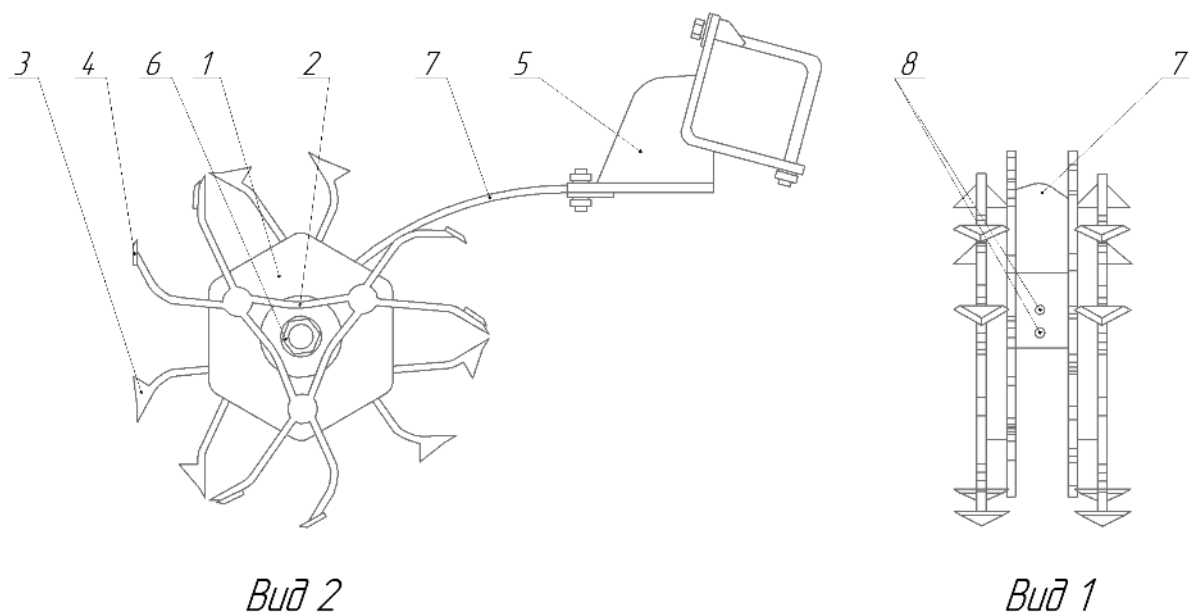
Вид 1 – вид в профиль, Вид 2 – вид сбоку
